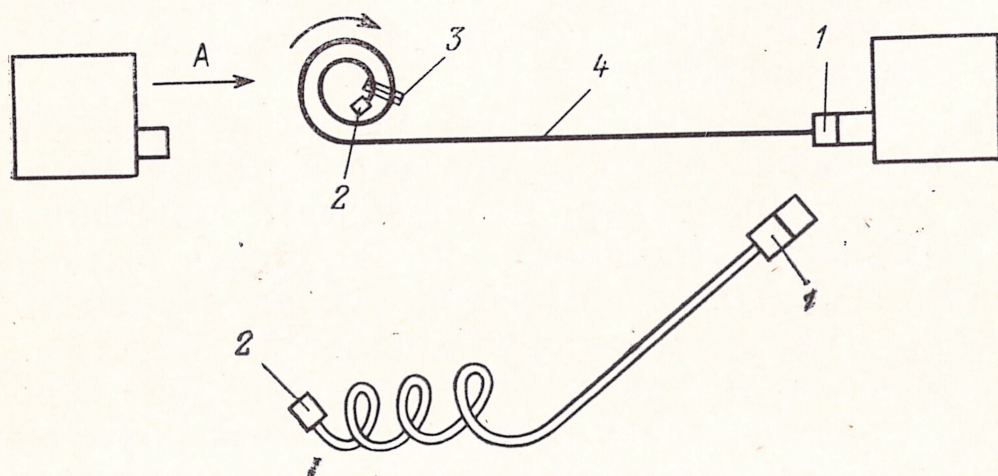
Схема укладки кабельного ствола в бухту (начало укладки у подвижного разъема).
